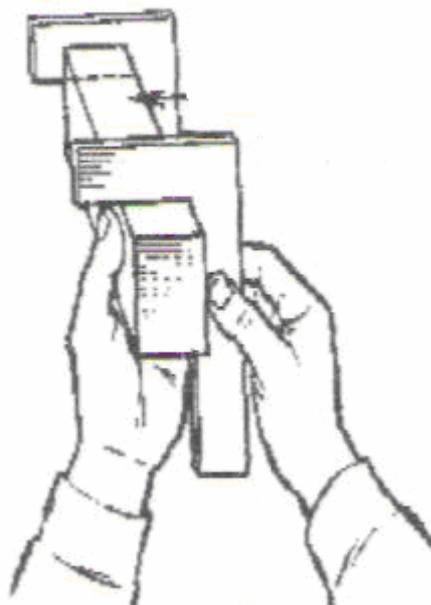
Опиливание широких поверхностей и проверка точности опиления
